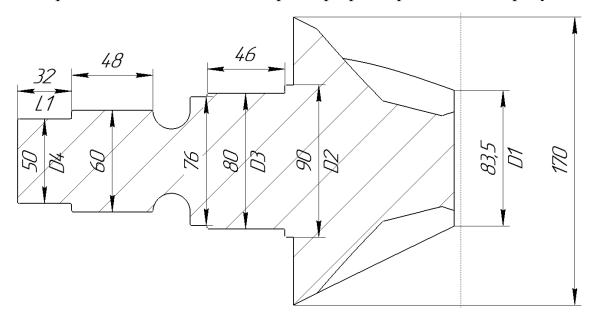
Чертёж конической вал-шестерни в разрезе
